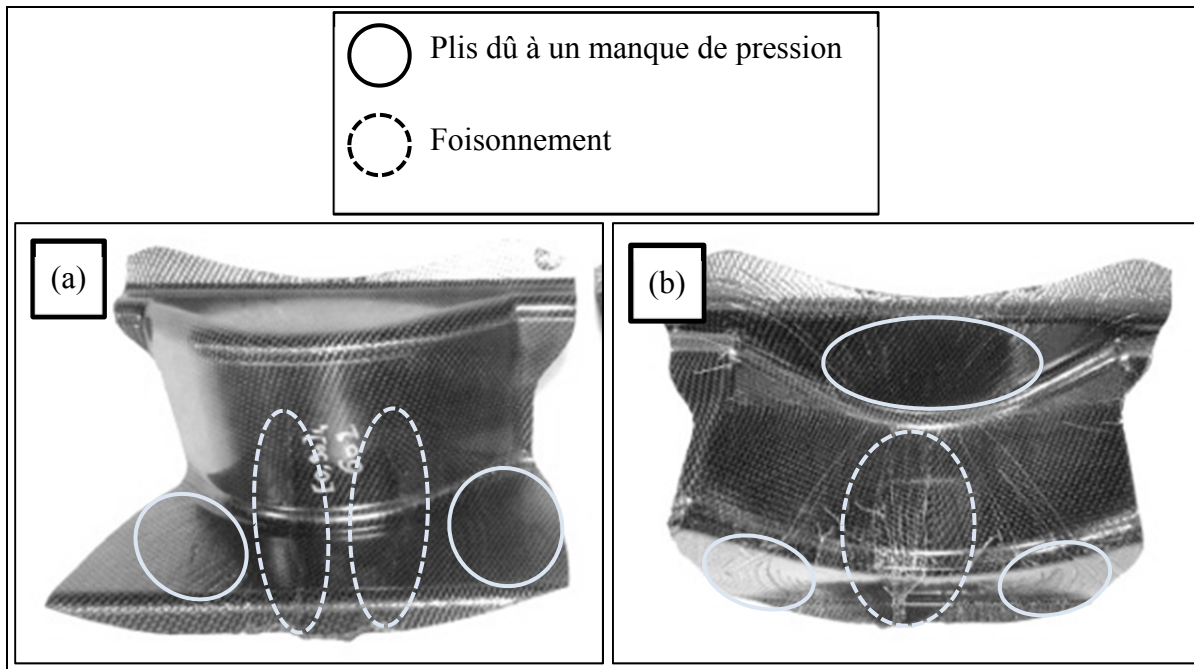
Face avant (a) et arrière (b) de la pièce moulée à partir de la plaque de séquence d'empilement  $(0,90)_4$  sans modification du film
